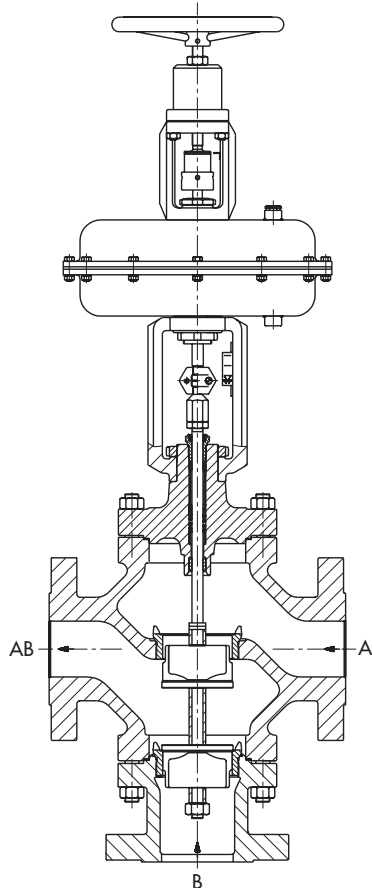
· Регулирующий клапан тип 3251-1 с пневматическим ручным дублиром, исполнение корпуса для Ду 50 ... 500, компоновка плунжера для смешительной функции приводом тип 3271 и дополнительным
